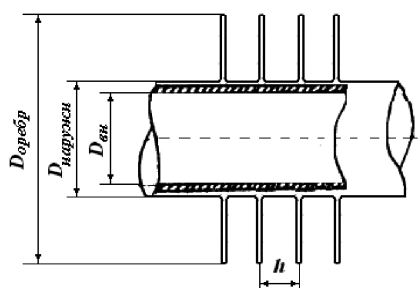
Основные конструктивные размеры оребренных труб:
